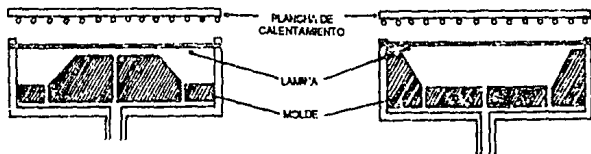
Molde macho y molde hembra utilizados en termoformado. (Ref. 4).
